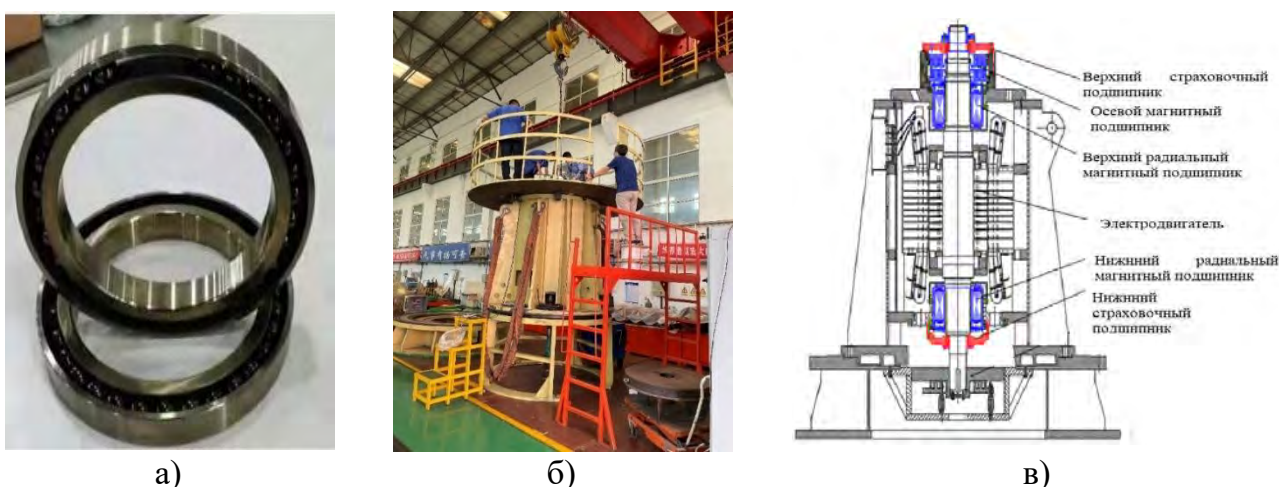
Страховочные подшипники и испытательный стенд: а) страховочный подшипник; б) испытательный стенд; в) схема испытательного стенда
